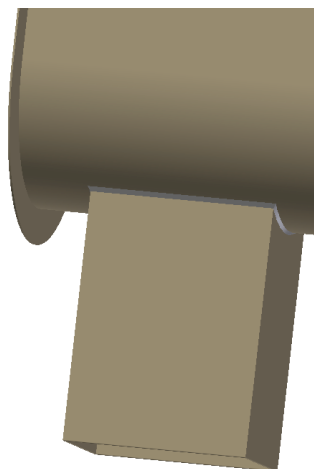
30 Soldadura de filete entre el canal y la artesa.
